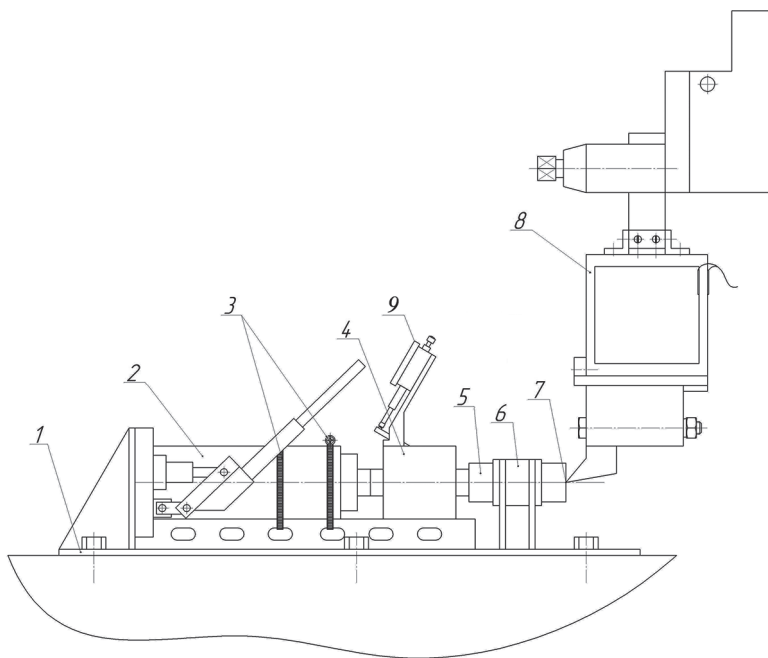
Схема оснастки для калибровки измерительной головки станда
